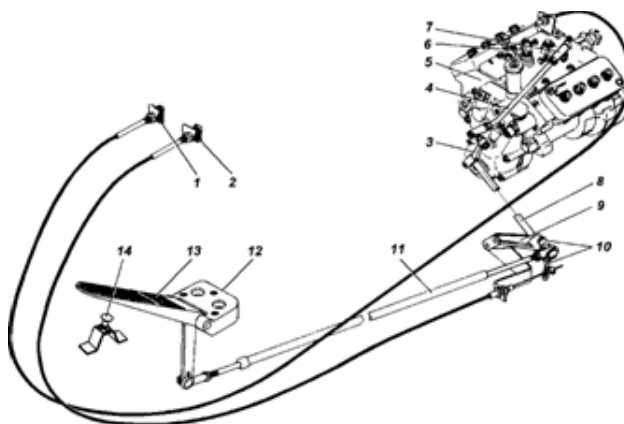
Привод управления подачей топлива: 1 – рукоятка тяги останова двигателя; 2 – рукоятка тяги ручного управления подачей топлива; 3, 10 – задние рычаги; 4 – тяга рычага управления регулятором; 5 – ТНВД; 6 – рычаг останова двигателя; 7 – рычаг управления регулятором; 8 – поперечный валик; 9 – задний кронштейн; 11 – телескопическая тяга; 12 – кронштейн педали; 13 – педаль; 14 – регулировочный болт
